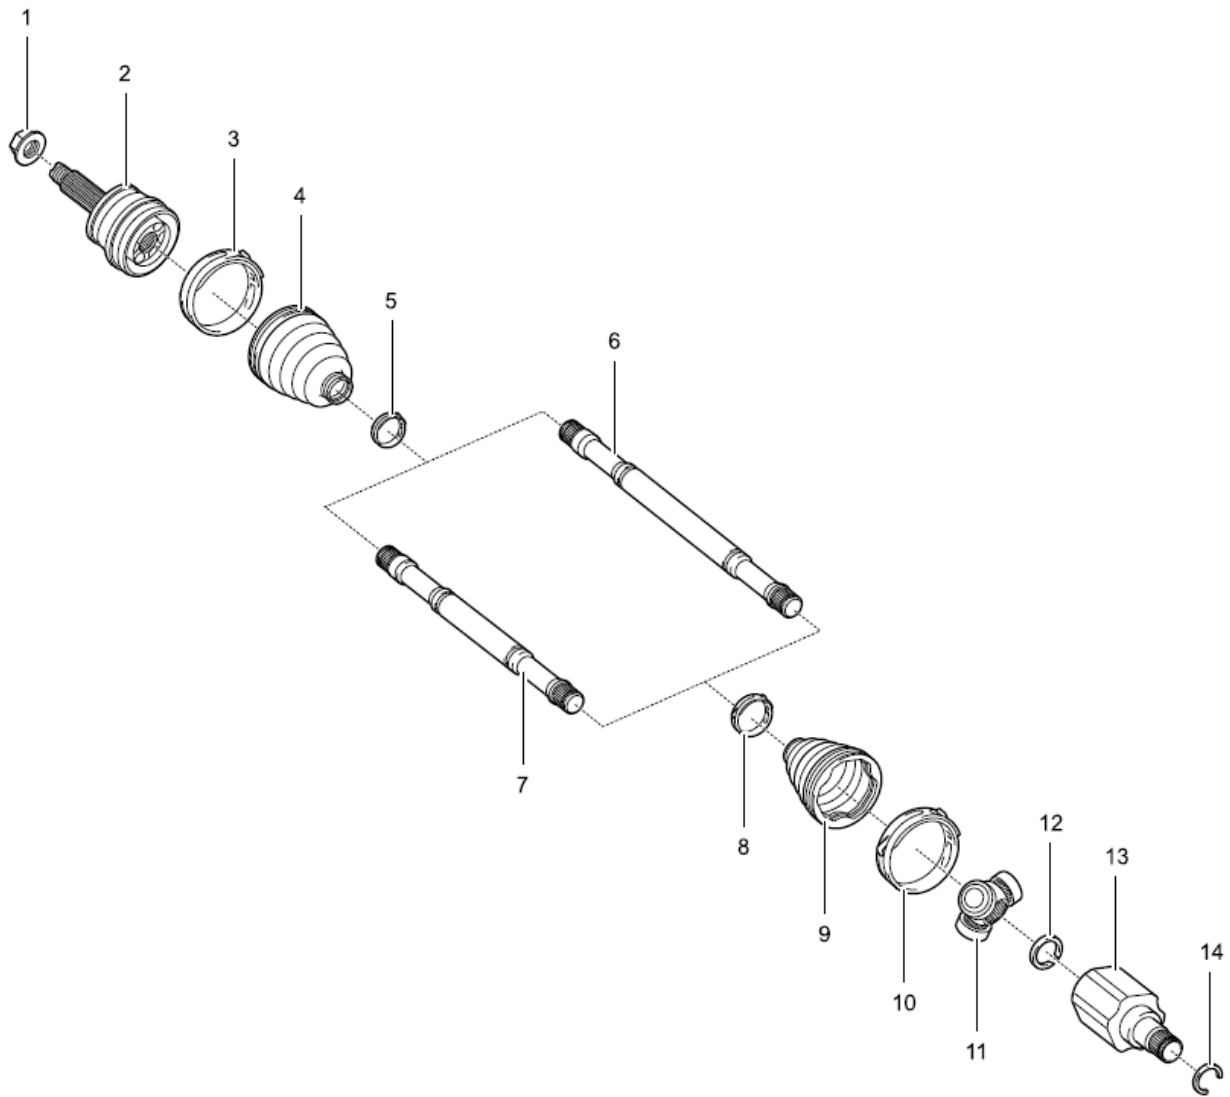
Пристрій валу привода колеса CHERY Tiggo5:
